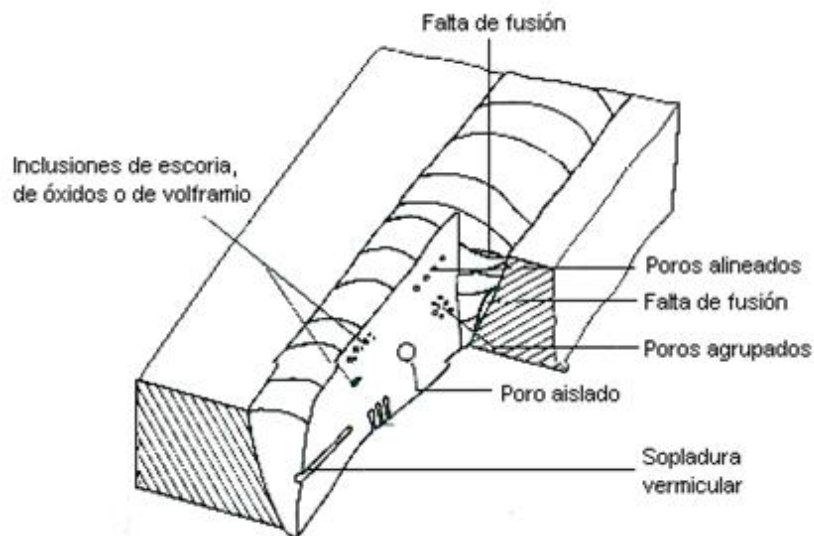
Defectos producidos en la soldadura por los efectos de la longitud del arco.
